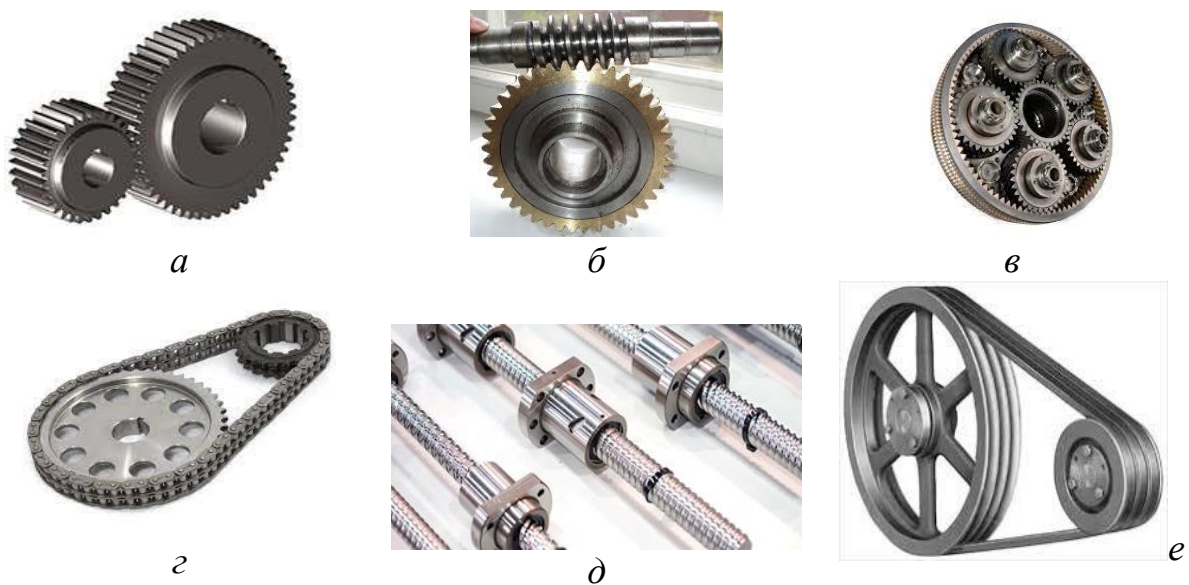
Зразки типових механічних передач: *а* – циліндрична; *б* – черв'ячна; *в* – планетарна; *г* – ланцюгова; *д* – гвинт-гайка; *е* – пасова
